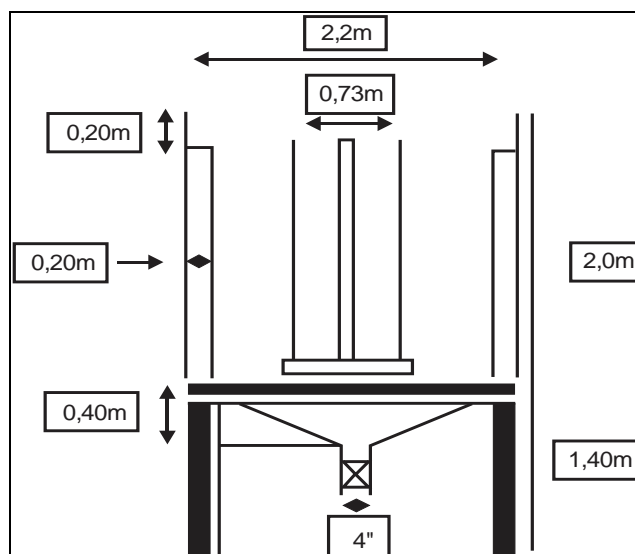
Esquema de dimensionamiento del tanque de agitador
